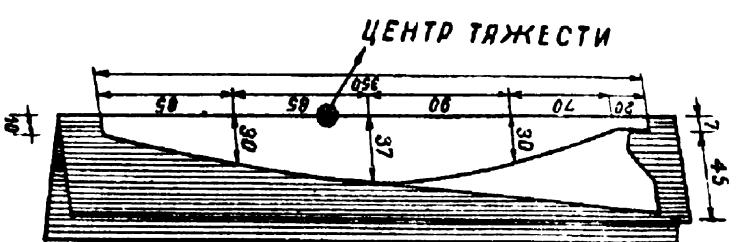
Изготовление чертежа корпуса гидропневматической ракеты
